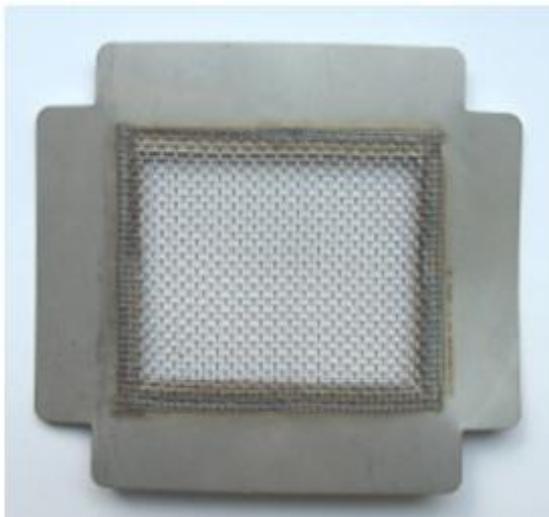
Boîte de stérilisation assemblée par soudage à la molette
